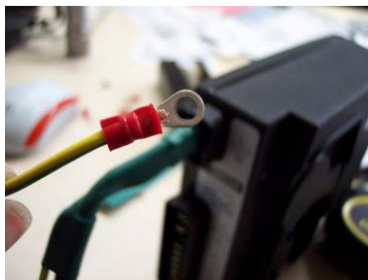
Деталь соединения кабеля заземления на металлической части компрессора
